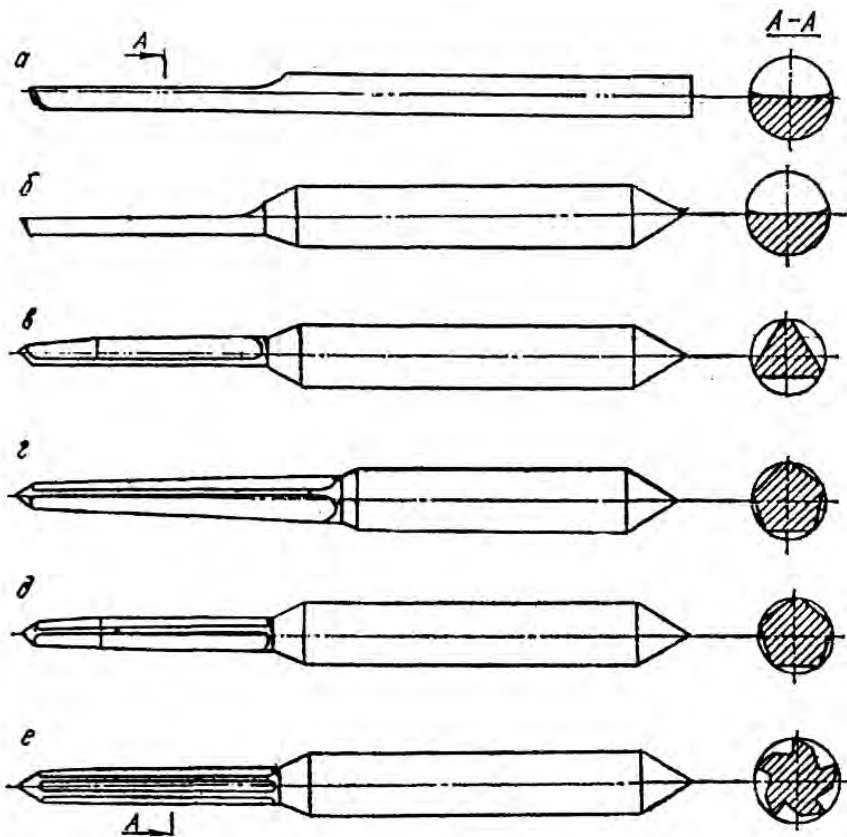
Развертки для обработки отверстий диаметром 0,1–3 мм:
